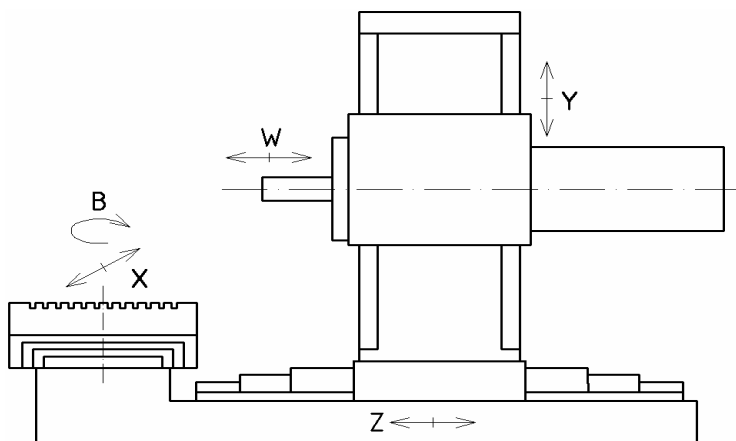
CNC horizontální frézovací a vyvrtávací stroj TK 6511 CNC <sup>14</sup>
